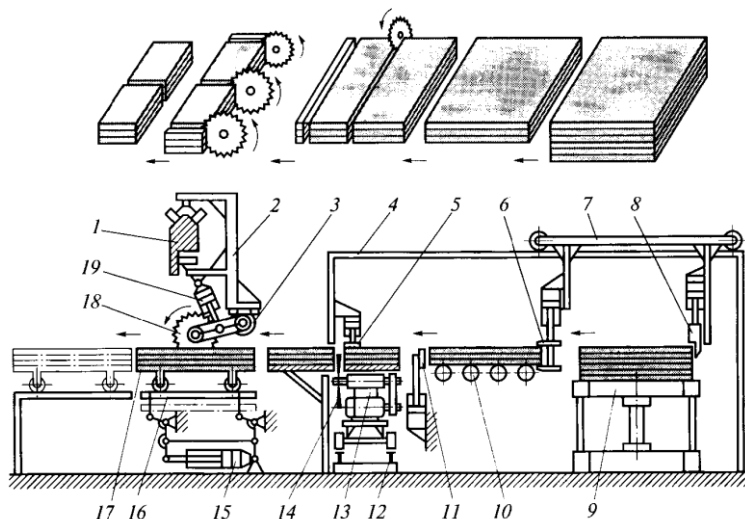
Схема форматно-розкрійного багатопилкового верстата: 1 – траверса; 2, 13 – супорти; 3 – електродвигун; 4, 12 – напрямні; 5 – притиск; 6 – затискачі-упори; 7 – завантажувальна каретка; 8 – штовхач; 9 – піднімальний стіл; 10 – пристрій базування пакета; 11 – упор; 14, 18 – пилки; 15, 19 – пневмоциліндри; 16 – піднімальні напрямні; 17 – каретка
